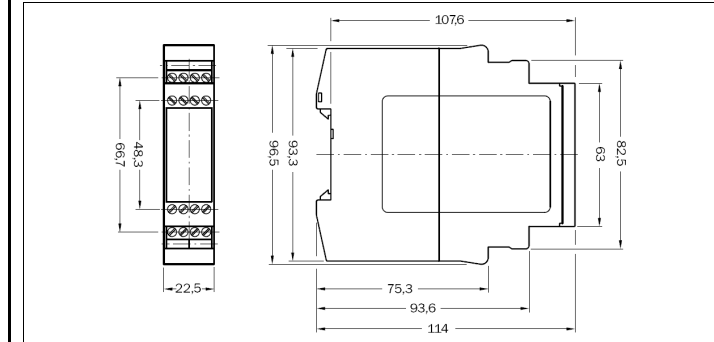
Croquis de dimensiones UE42-2HD con terminales de tornillo (mm)
